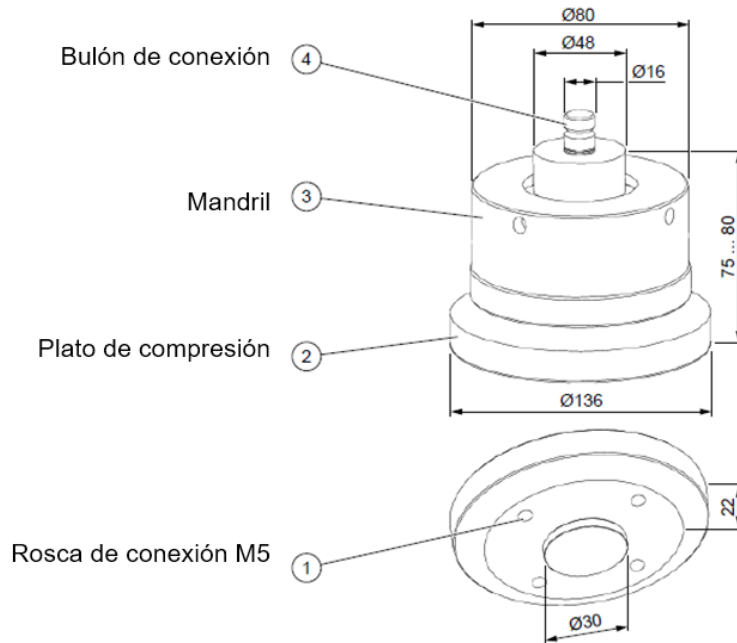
Dimensiones de los utillajes de compresión de la máquina Zwick.
